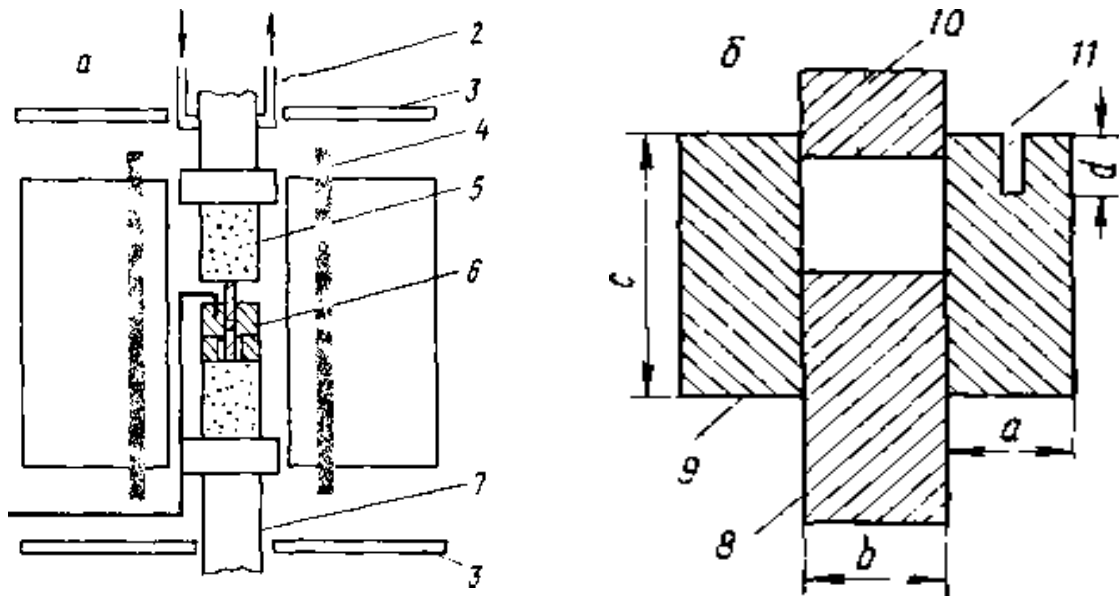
Схема установки (а) и прессформы (б) для горячего прессования: 1 — термопара; 2 — система водного охлаждения; 3 — металлическая теплоотражающая плита; 4 — нагревательный силитовый стержень; 5 — корундовый стержень для передачи давления; 6 — прессформа; 7 — подвижный пуансон; 8 — нижний пуансон; 9 — корпус формы; 10 — верхний пуансон; 11 — щель для термопары
